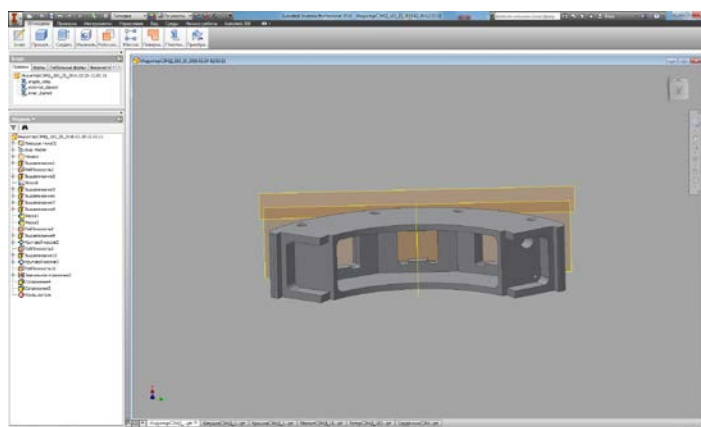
Эскиз цифровой модели корпуса индуктора СЭМД 183-25
